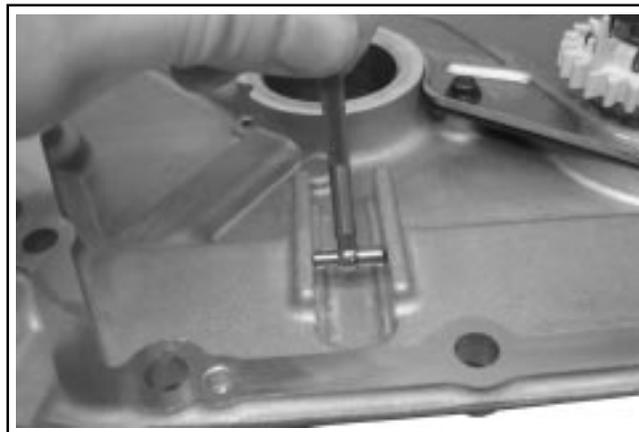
Mesure de la largeur du canal de guidage de la plaque de fermeture.
